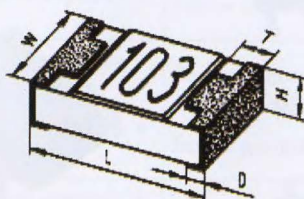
Цифровая маркировка на корпусе SDM элементов
